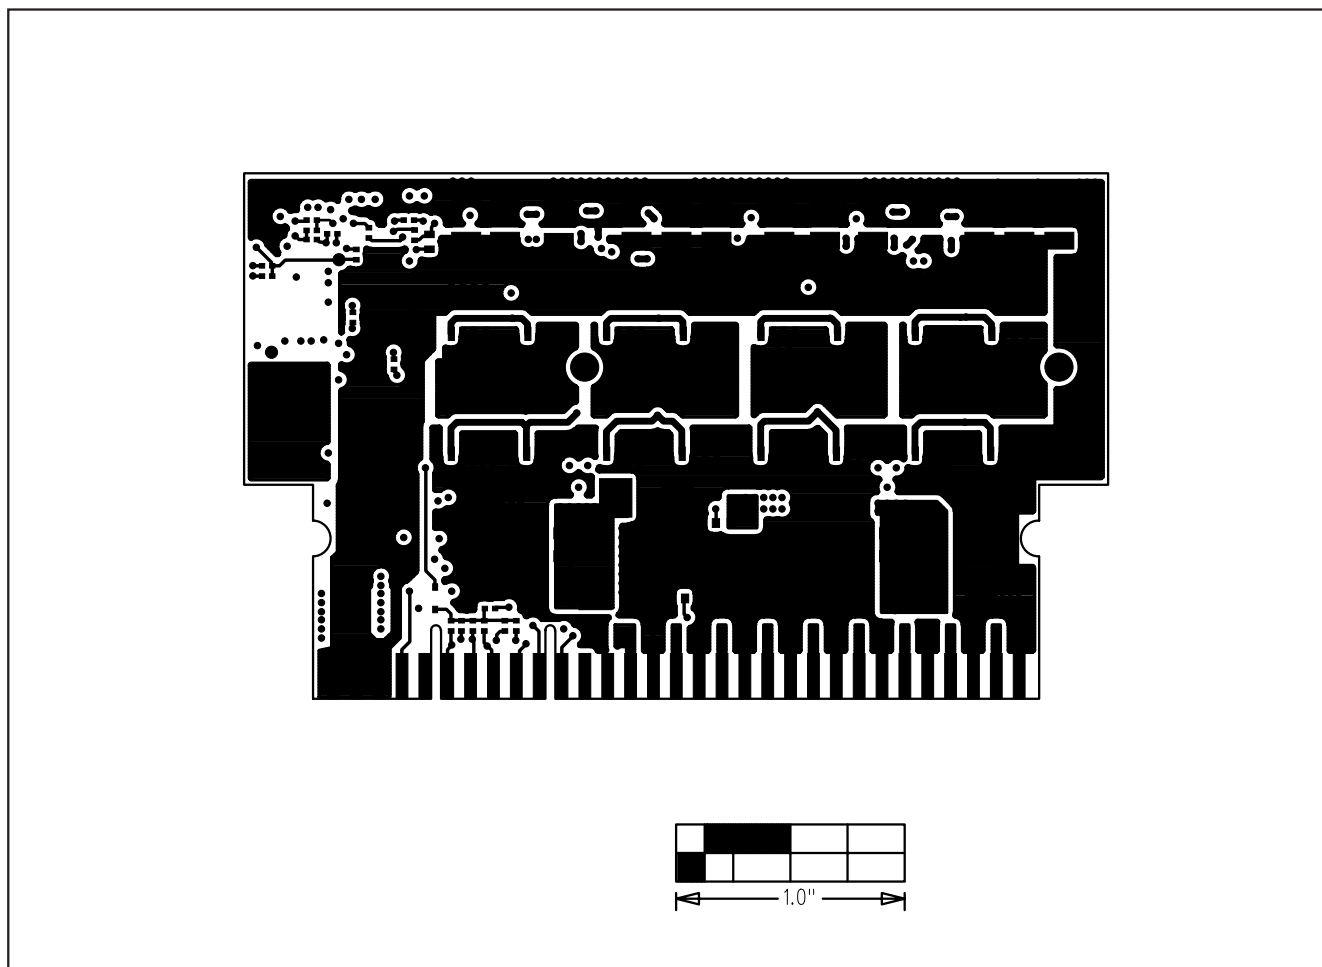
MAX8525 评估板 PC 板布线——焊接面
